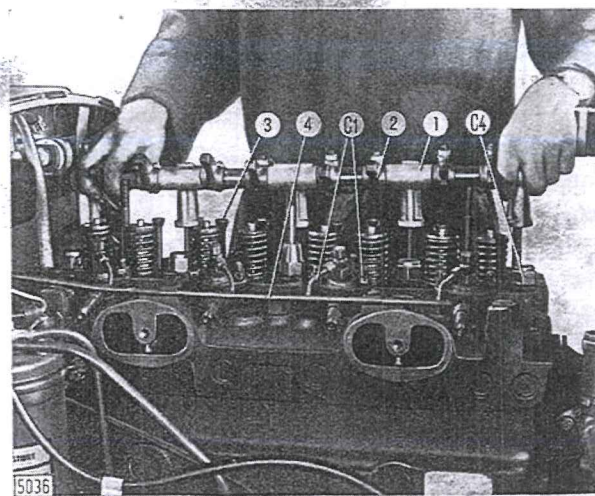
Distacco del gruppo bilancieri con motore montato sul trattore.
